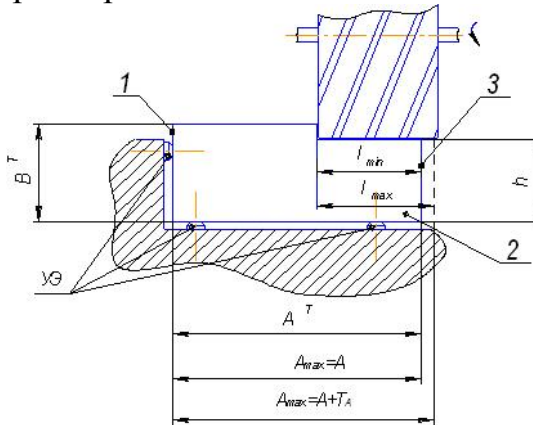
Схема для определения погрешности базирования размеров призматической заготовки h и l
